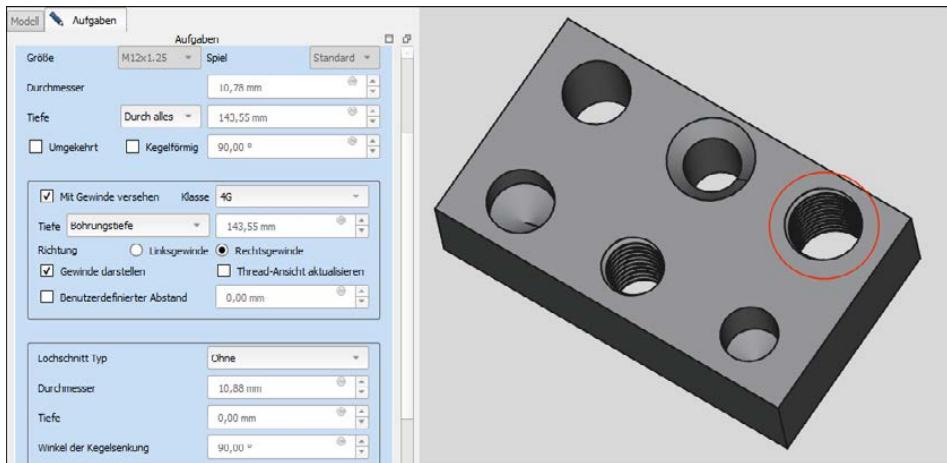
Varianten beim Werkzeug »Bohrung«
